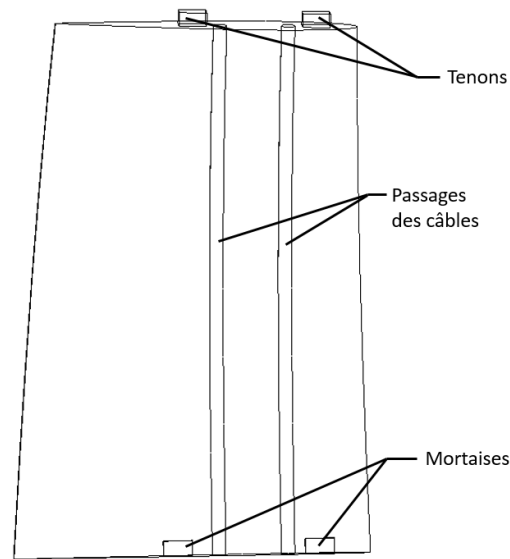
Principe d'assemblage entre les différentes sections de pale
